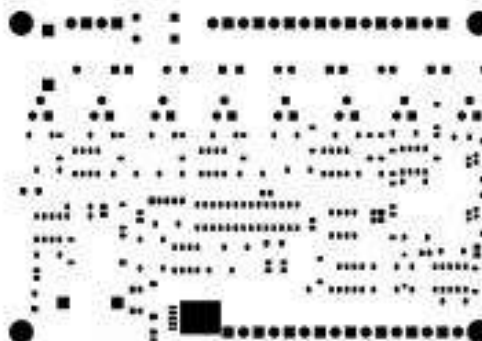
Tarjeta capa de antiofen lado de soldaduras
